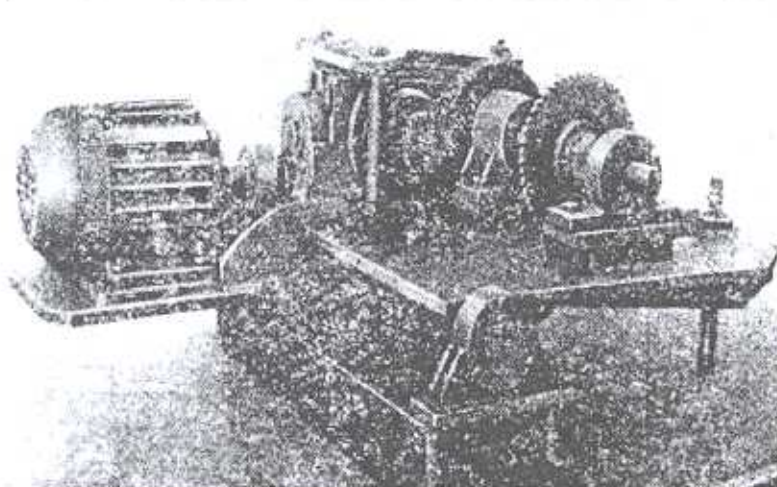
Приспособление для фрезеровки шлицев на бочке ротора
